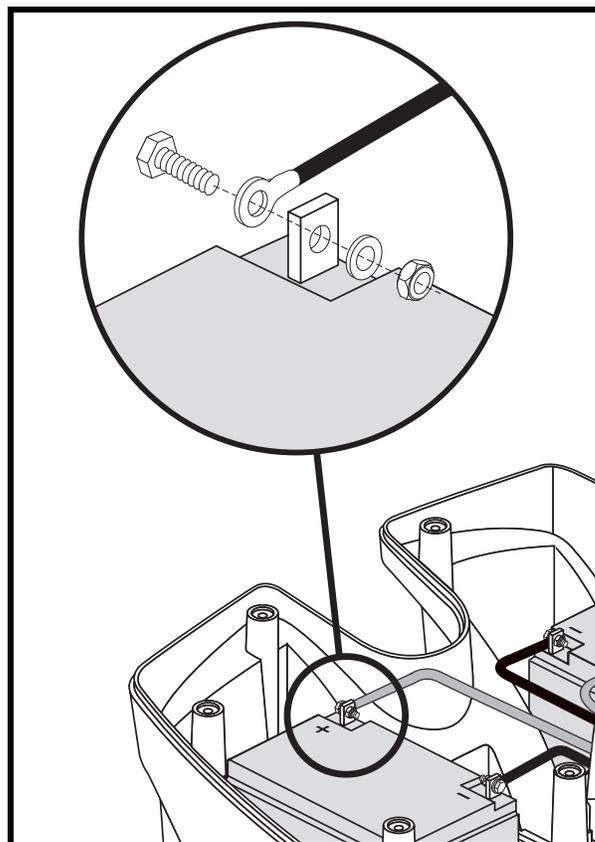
Desconexión del cable de una batería de 17-22 amperios
